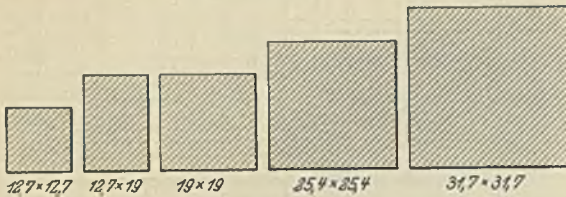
Geprüfte Werkzeugquerschnitte.
